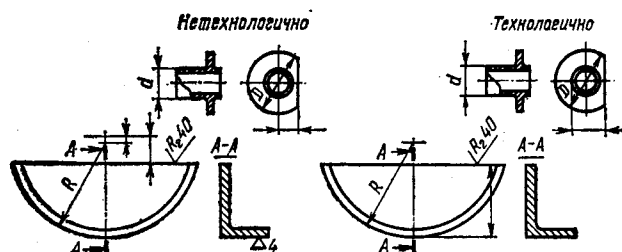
Простановка размеров на деталях с обрабатываемыми лысками.
